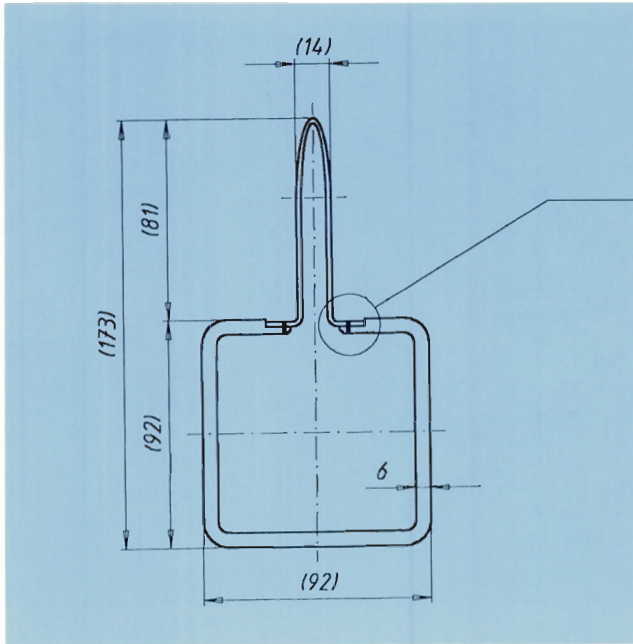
„Schlüsselloch“-Strahlrohrkammer für den Undulator im PETRA-Ring. Die Kammer besitzt eine Länge von 4.2 m, wurde aus gekantetem CrNi-Blech gefertigt und mit einer Geschwindigkeit von 3.5 m/min verzugsarm laserstrahlgeschweißt. (42607/24)
